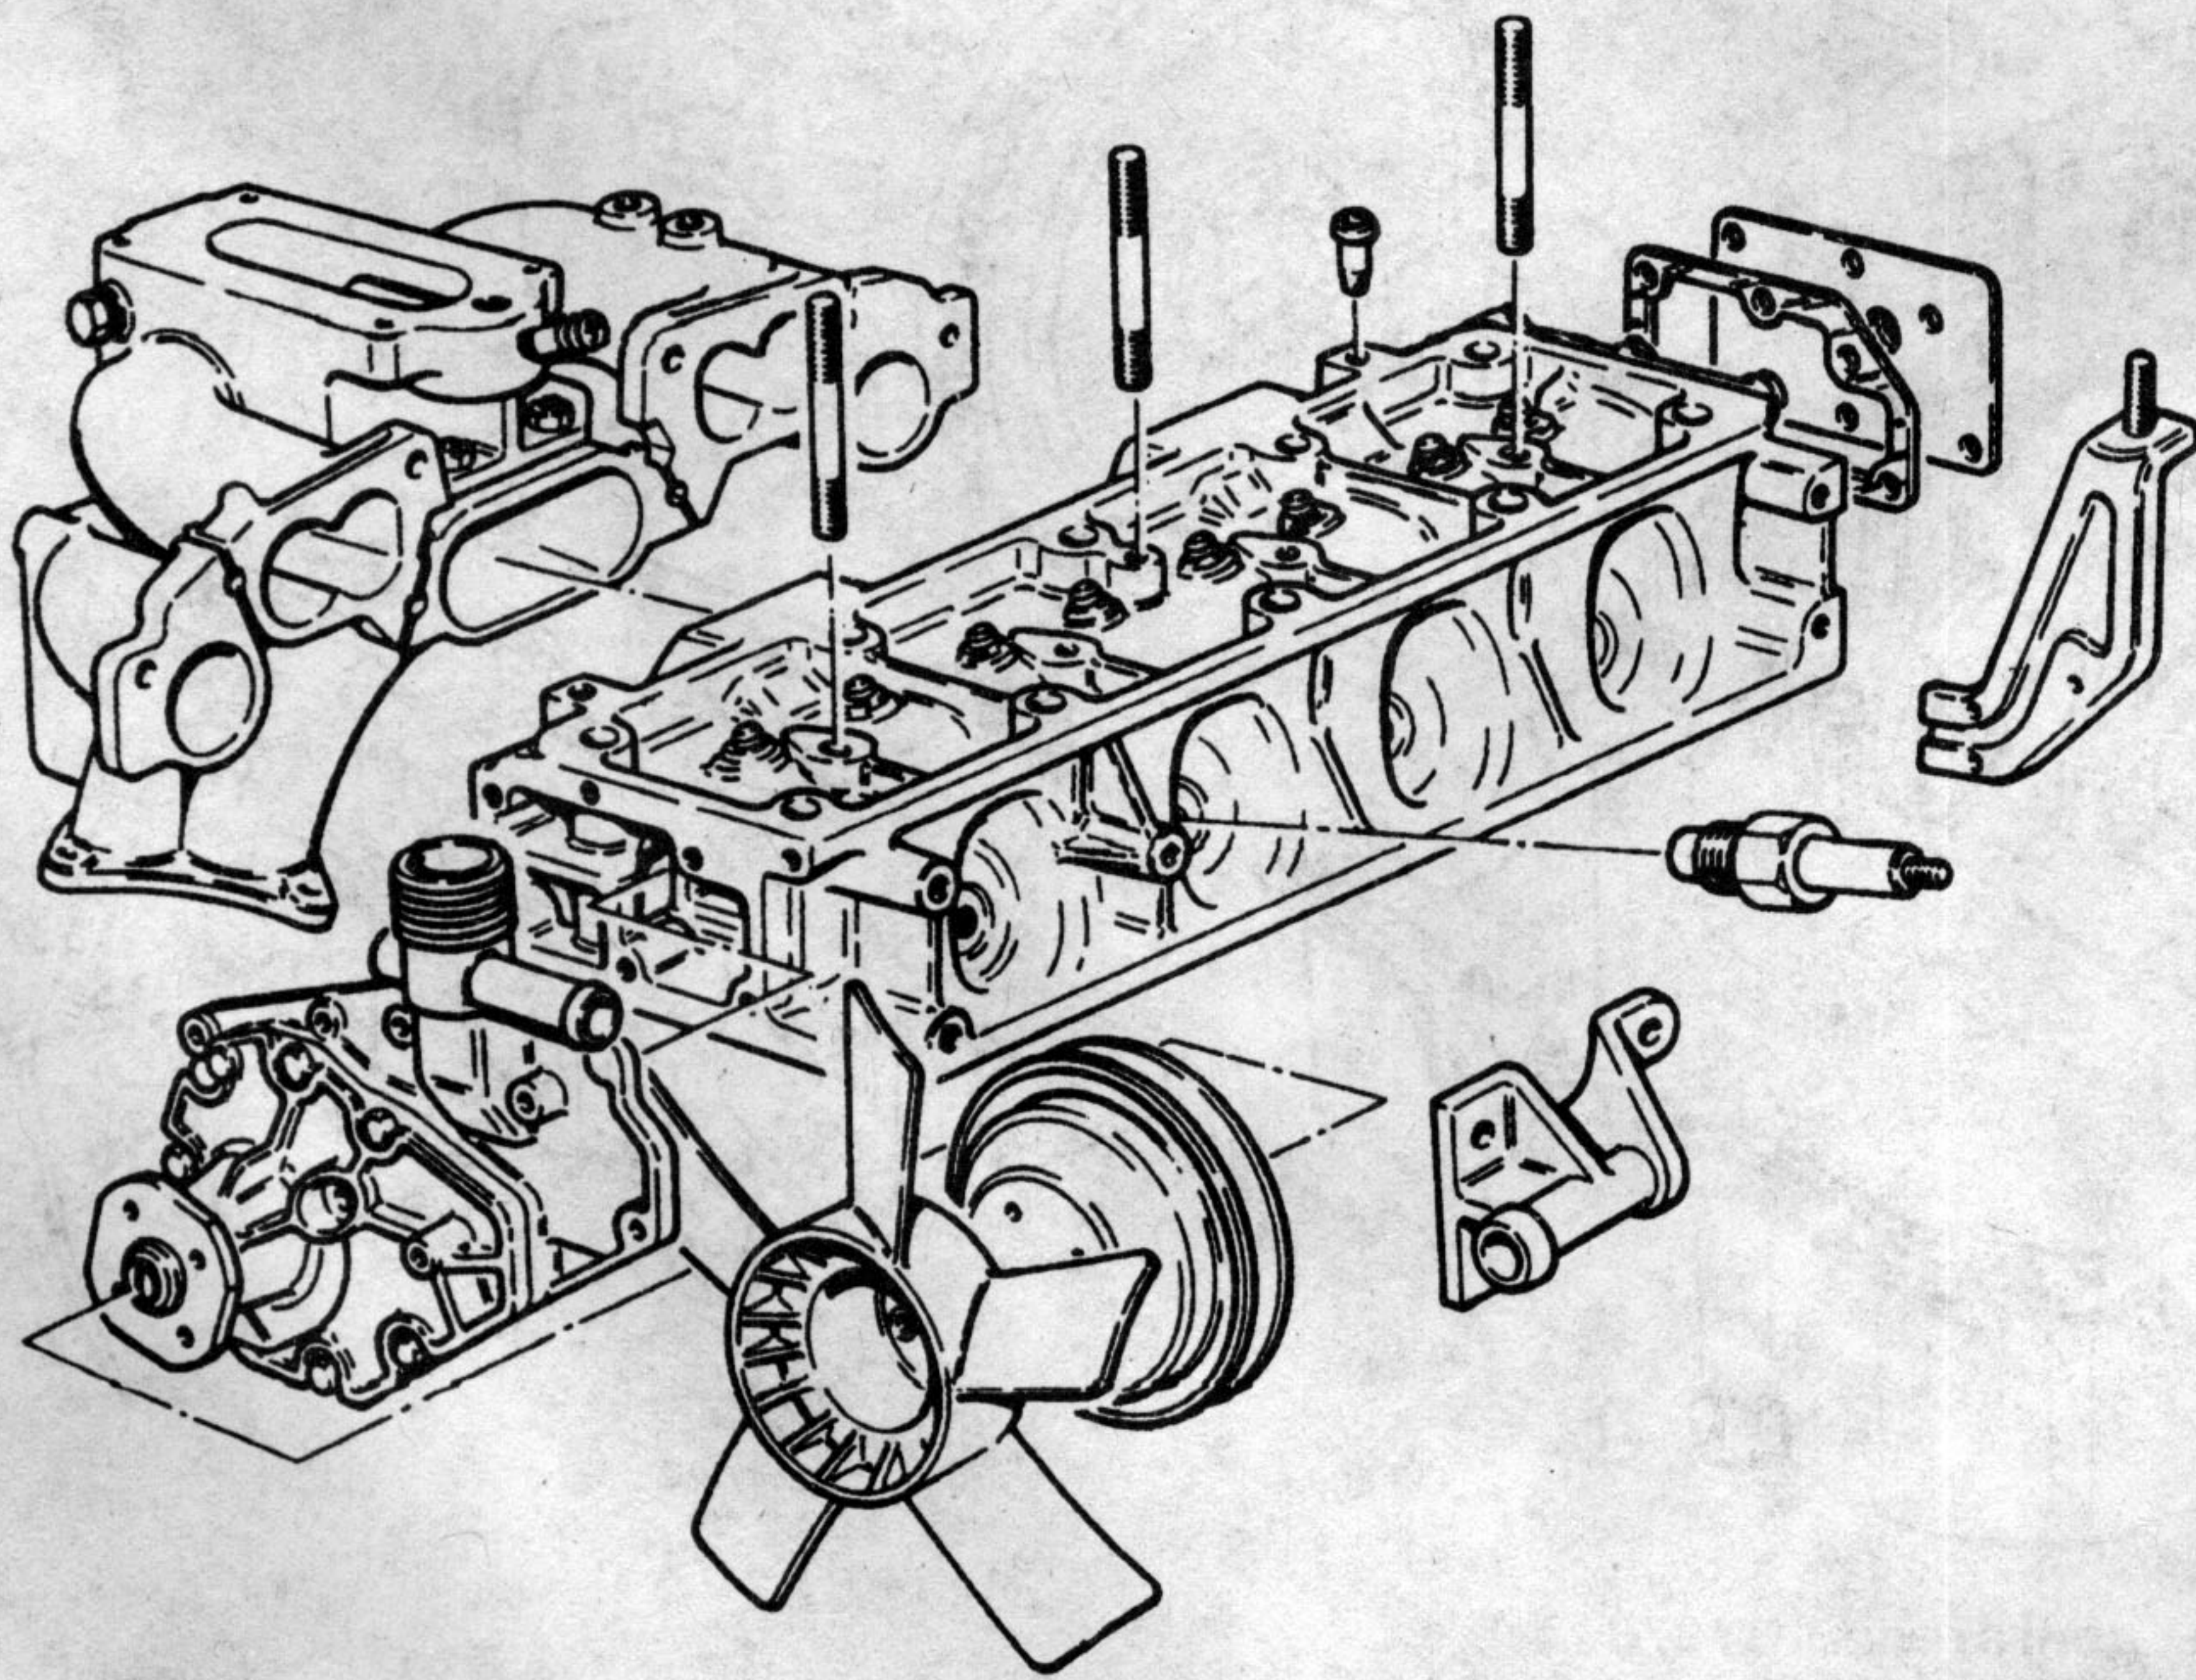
Головка блока цилиндров двигателя В13/В14 в разобранном состоянии
